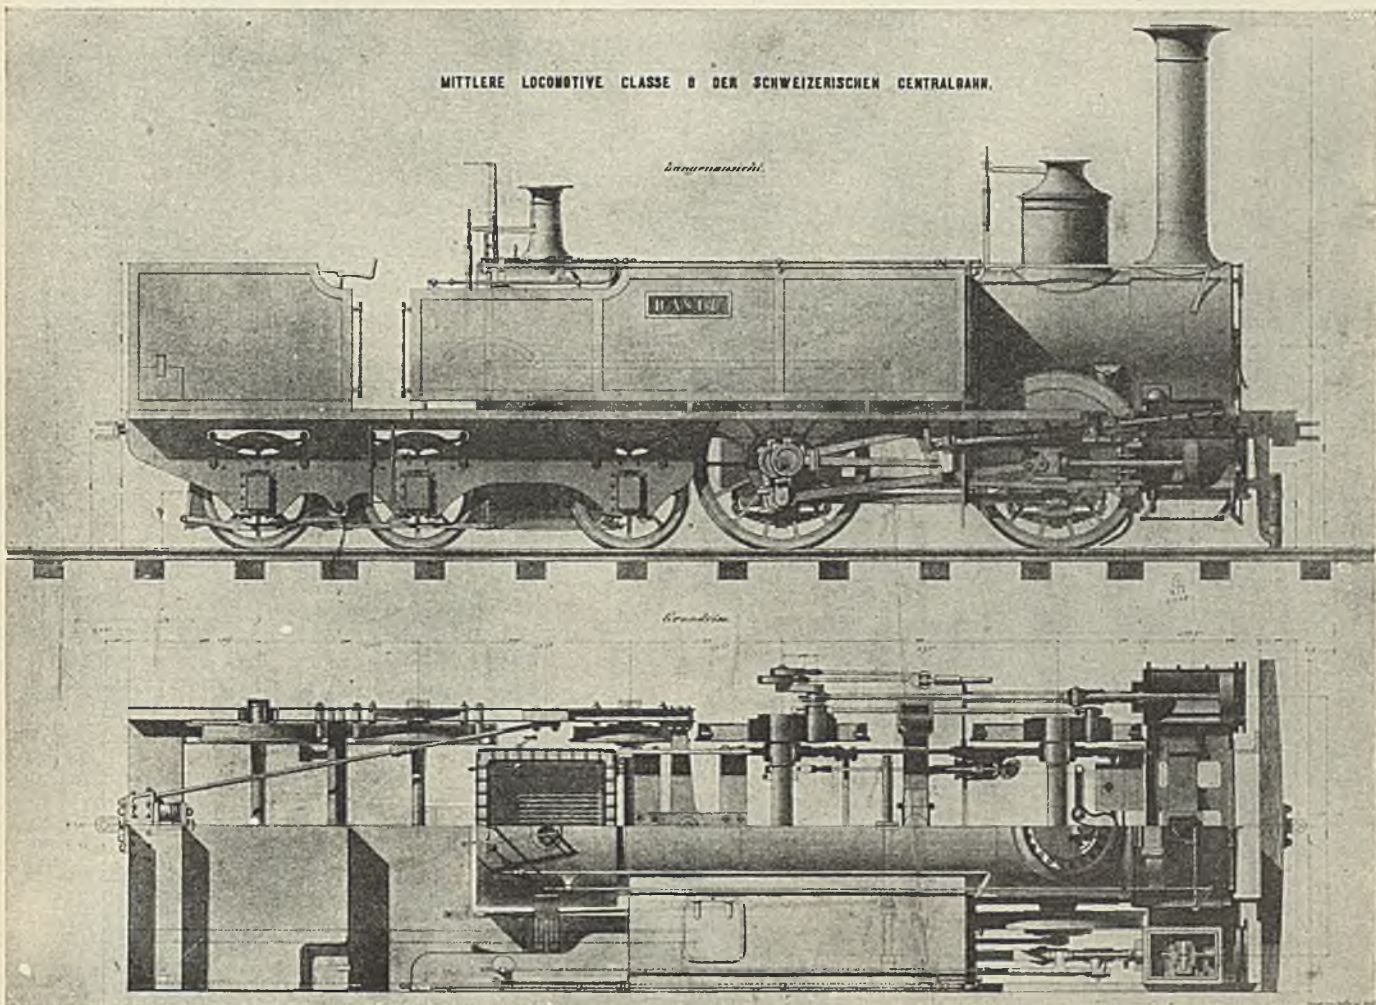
Längsansicht, 1/2-Wagrechtschnitt, 1/2 Grundriss.
